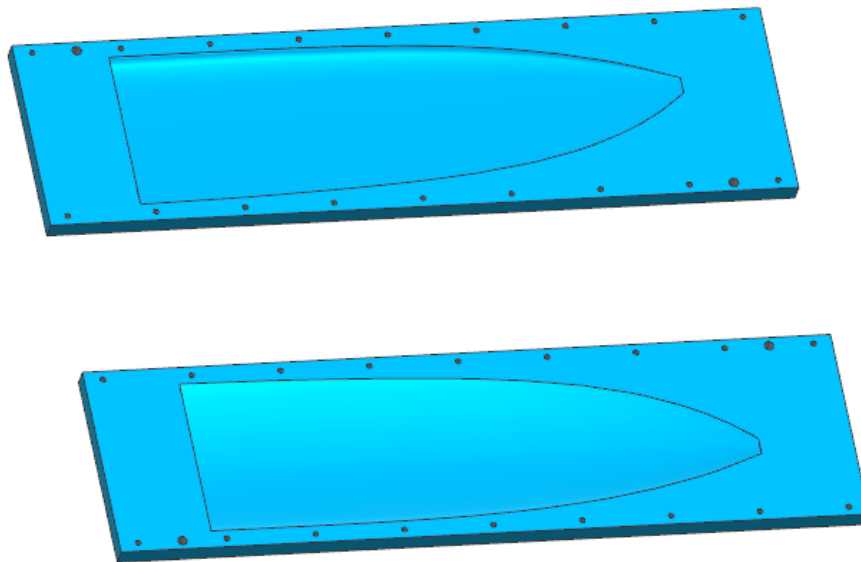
Diseño del molde del extremo del ala, cortando esta por el plano que pasa por el borde de ataque y el borde de salida.
